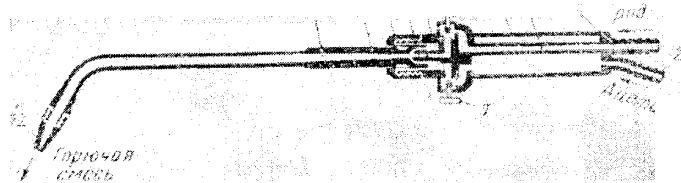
Инжекторная сварочная горелка
